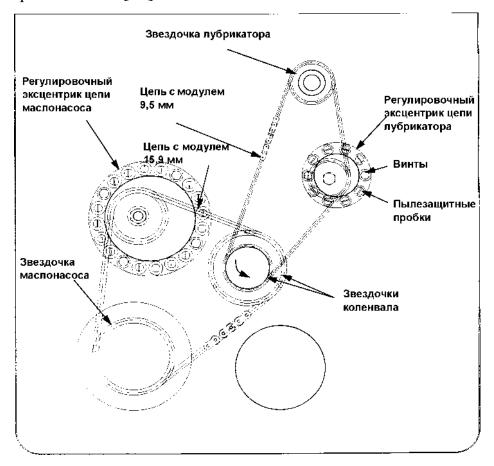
Цепной привод - стандартное направление вращения (вид со стороны привода вспомогательных механизмов)
